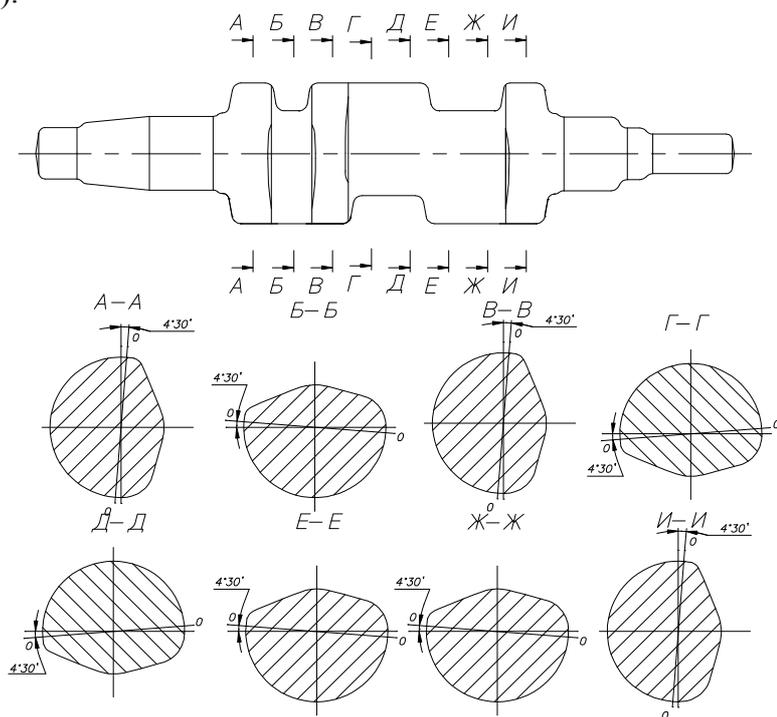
Чертеж горячей поковки до процесса выкрутки.
